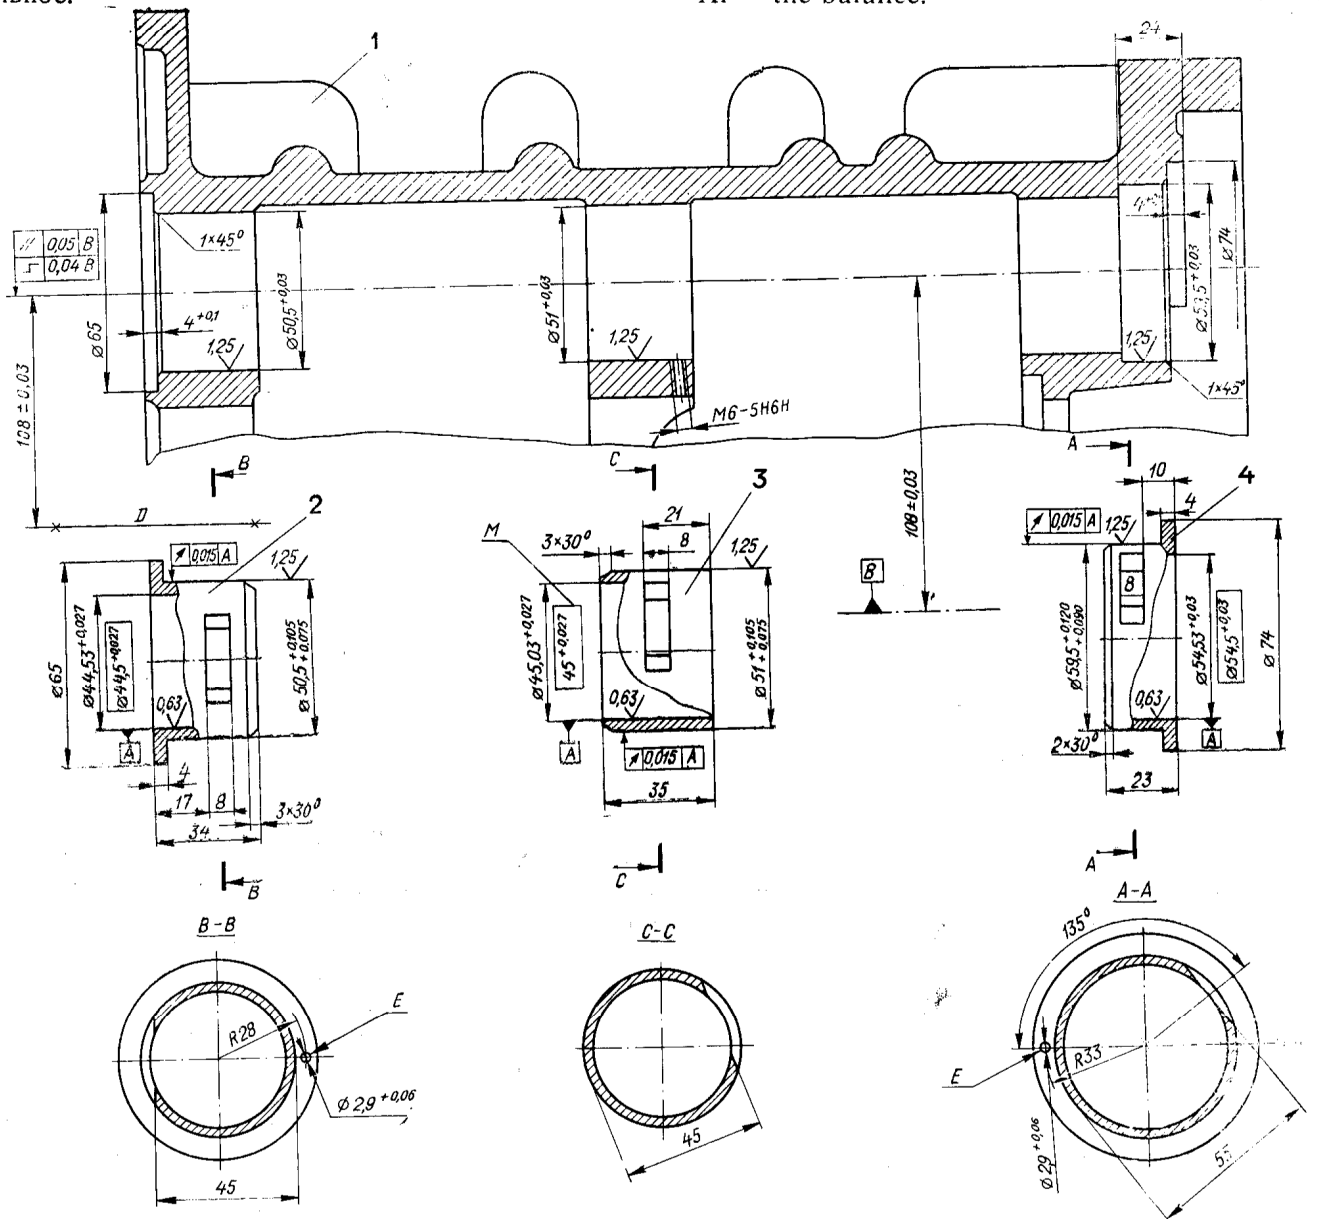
Расточка картера двигателя под ремонтные подшипники распределительного вала: 1 — картер коленчатого вала; 2, 3, 4 — ремонтные подшипники опор распределительного вала; D — ось коленчатого вала
